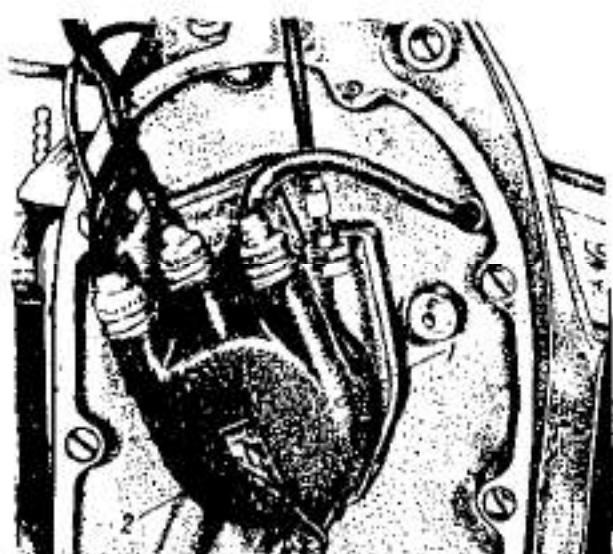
Прерыватель-распределитель ПМ05, установленный на двигателе:
